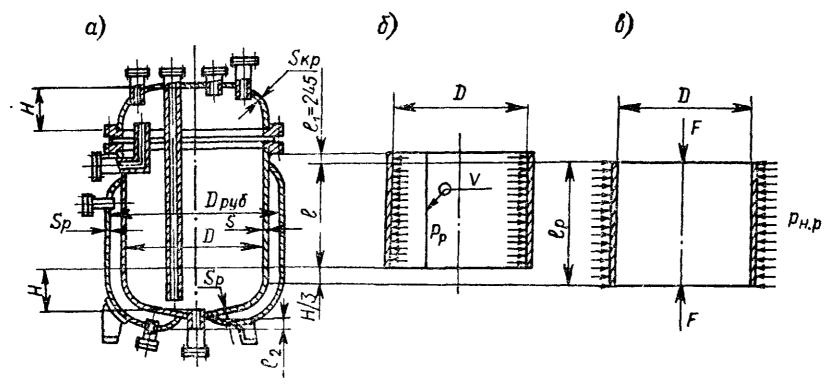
Рис. V. Вертикальный аппарат с эллиптическими днищем и крышкой, с рубашкой (а) и расчетные схемы цилиндрической обечайки его корпуса при действии в отдельности внутреннего давления (б) и давления в рубашке (в)
